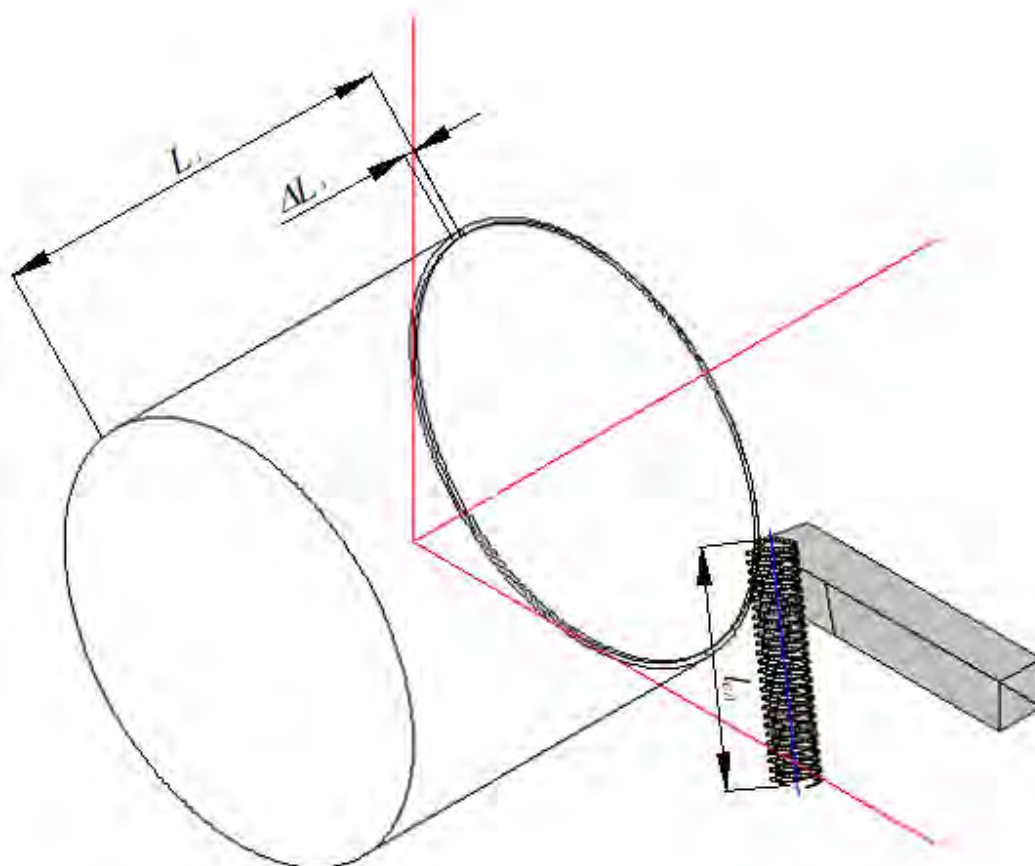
Схема разбиения обрабатываемой поверхности
